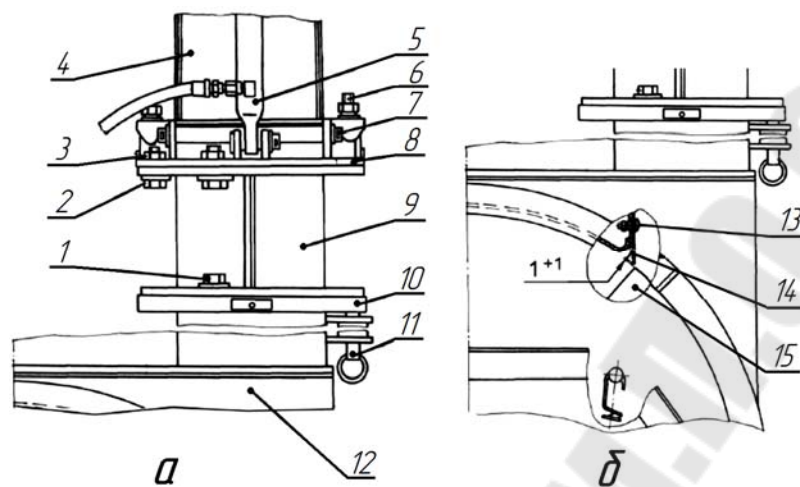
Схема установки проставки силосопровода: а – установка проставки силосопровода; б – механизмы регулировки зазора между лопатками; 1, 2, 6, 13 – болты; 3 – гайка; 4 – силосопровод; 5 – гидроцилиндр поворота силосопровода; 7 – ось; 8 – опора; 9 – проставка; 10 – кольцо механизма поворота; 11 – фиксатор; 12 – корпус швырляки; 14 – пластина; 15 – лопатка
